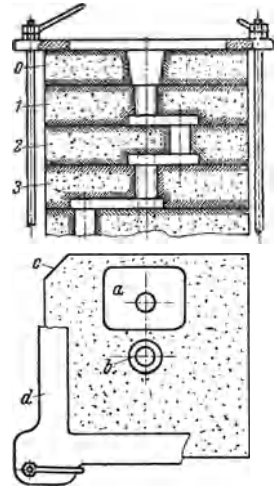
Aufbau der Form. 0 = oberster Flachkern für Einguß und Steiger; 1, 2, 3 usw. = Kerne für die einzelnen Kurbeln; a = Einguß für steigenden Guß; b = Steiger; c = Kernsicherung (vgl. Abb. 314); d = Spannrahmen.
